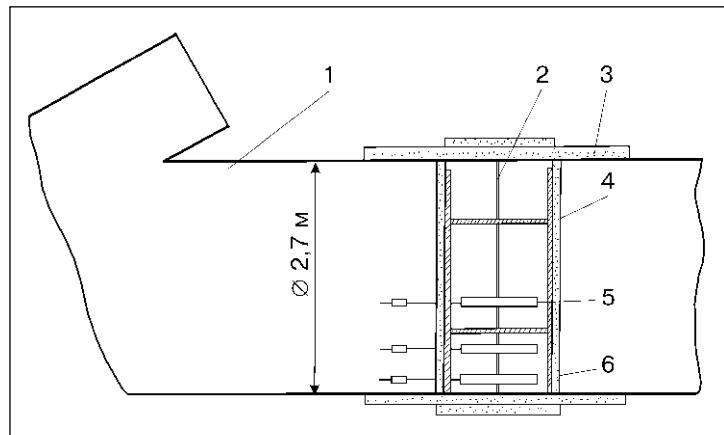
Общий вид трубного узла при внутренней термообработке: 1 — трубный узел; 2 — сварной шов; 3 — внешняя теплоизоляция; 4 — теплоизоляционная перегородка; 5—6 — рядные электронагревательные элементы; 6 — металлоконструкции, переборки
